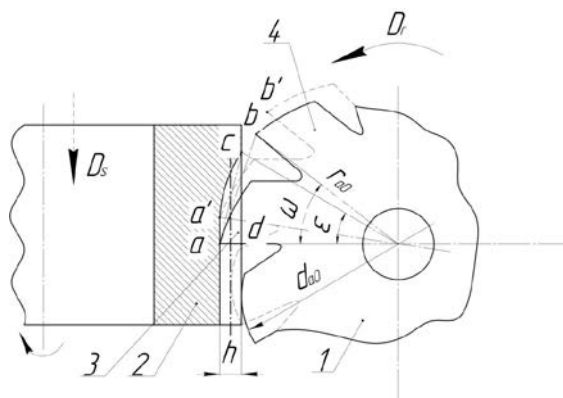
Схема зубофрезерования цилиндрических шестерён с импульсной подачей
